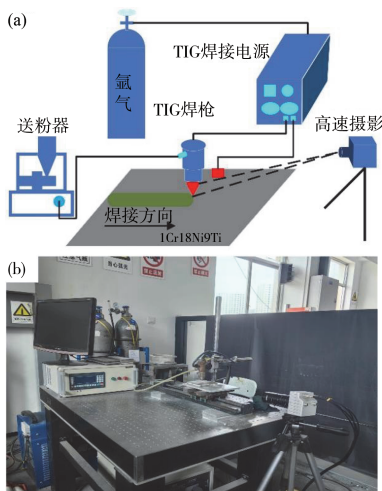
PPCA-TIG 焊接试验平台:(a) 示意图;(b) 实物图
